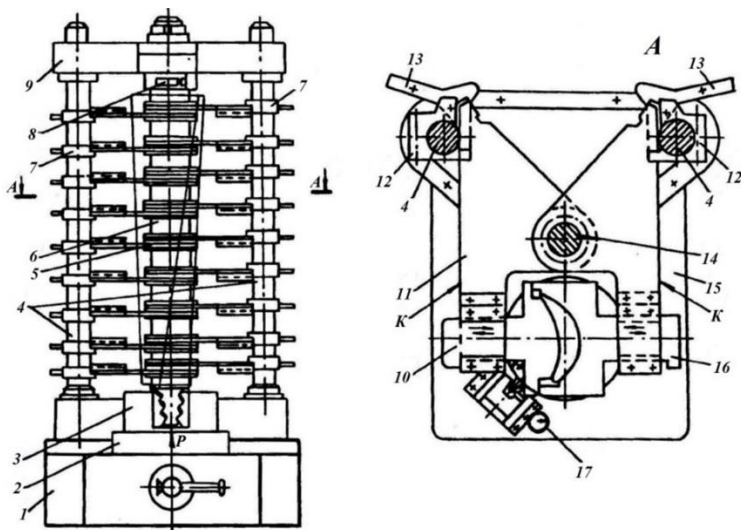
Приспособление для контроля профиля пера крупногабаритных лопаток
